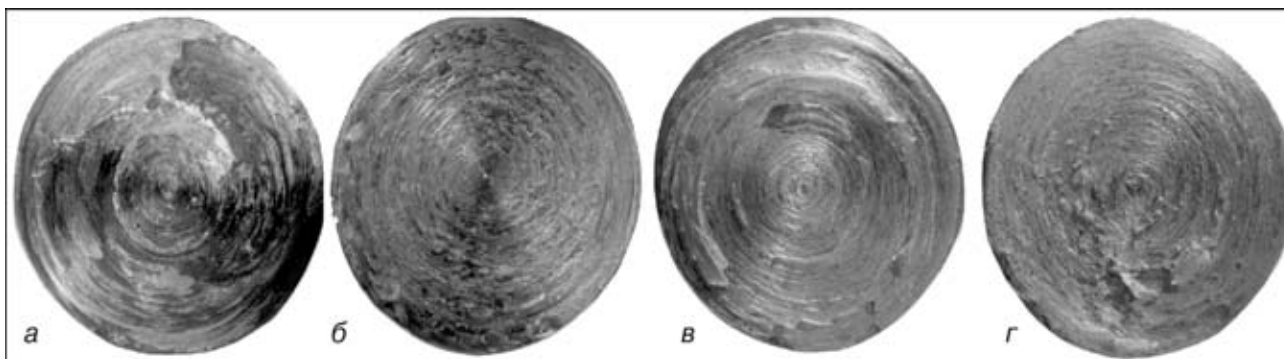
Поверхности изломов со стороны медной заготовки соединений меди с алюминием, полученных при токарной обработке с использованием смазки за 120 (а), 0,5 ч до сварки (б) и токарной обработке без использования смазки за 120 (в), 24 ч до сварки (г)
